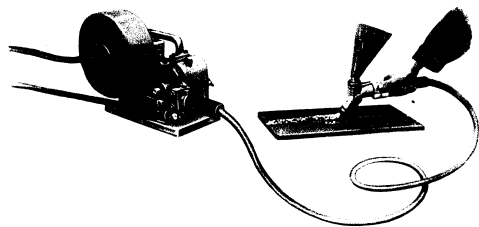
Податчик проволоки полуавтомата ДПП-5 и держатель ДПП-5 при сварке стыкового шва
